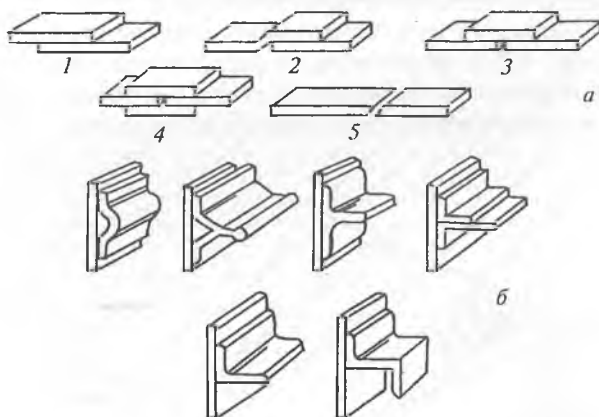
Типы клеевых соединений: *а* — листы обшивки; 1 — одинарная нахлестка; 2 — нахлестка с подсечкой; 3 — встык с односторонней накладкой; 4 — встык с двухсторонней накладкой; 5 — на "ус"; *б* — обшивка со стрингерами различного профиля
